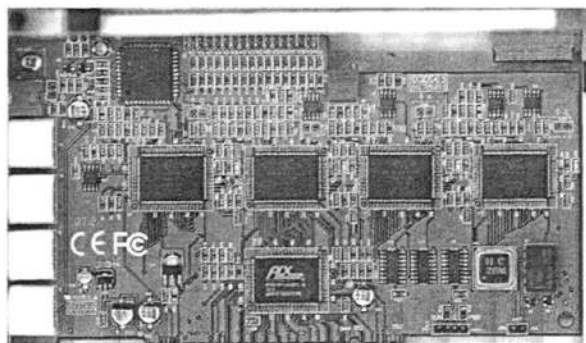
本文拼接算法得到完整的 PCB 板概略图
